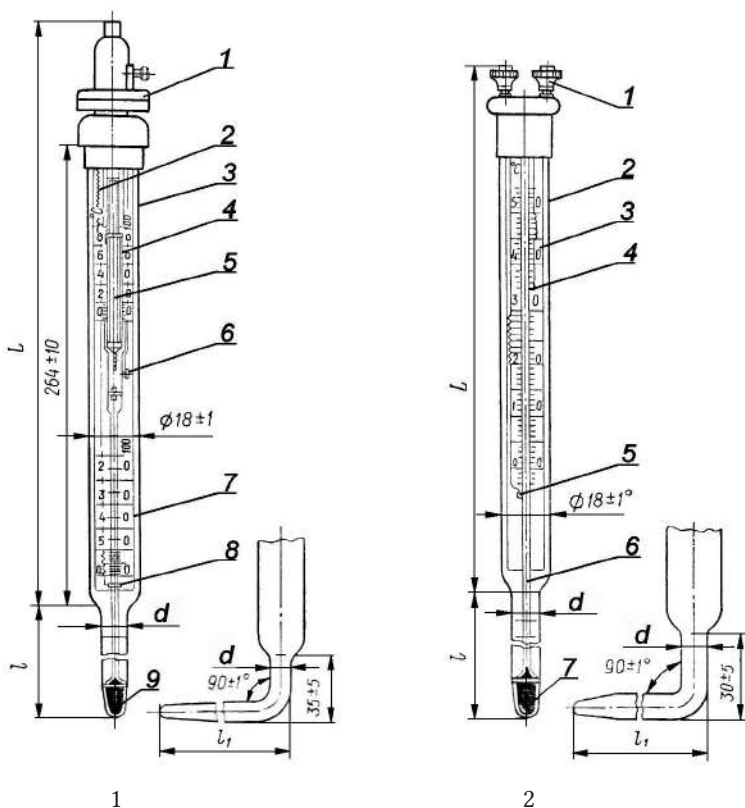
(1). Термоконтактатор з рухливим контактом: 1 — постійний магніт; 2 — мідний дріт; 3 — оболонка; 4 — верхня шкала; 5 — мікровинт; 6 — рухливий контакт; 7 — нижня шкала; 8 — непорушний контакт; 9 — резервуар; l — довжина нижньої частини; L — довжина верхньої частини; l_1 — довжина вигнутої частини; d — діаметр нижньої частини.
